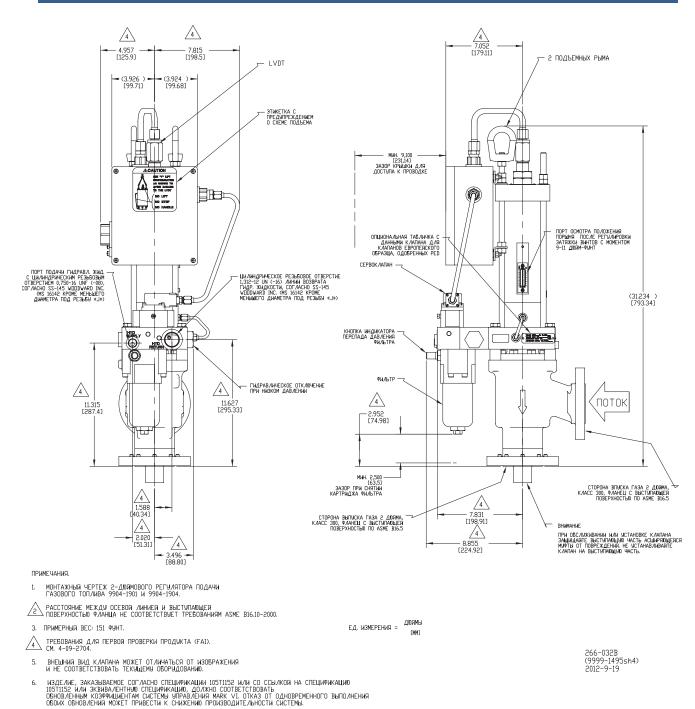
Габаритный чертеж регулятора SonicFlo (2 дюйма, класс 300)
